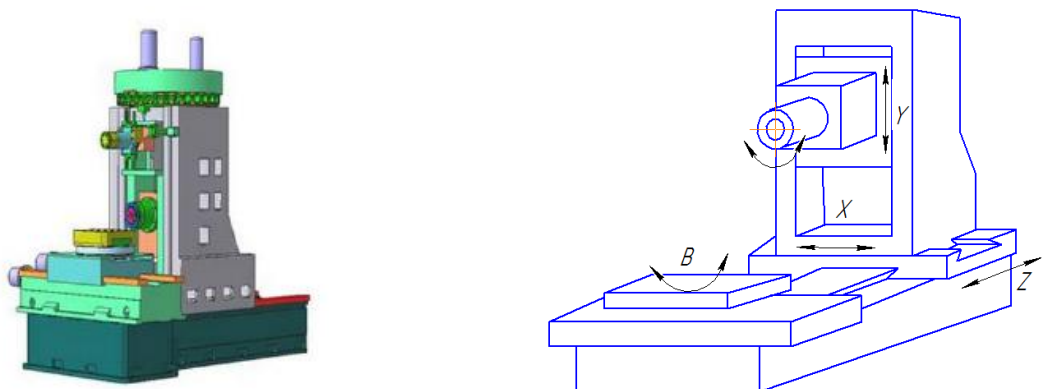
Загальний вигляд та компоновання верстату IP500ПМФ4
